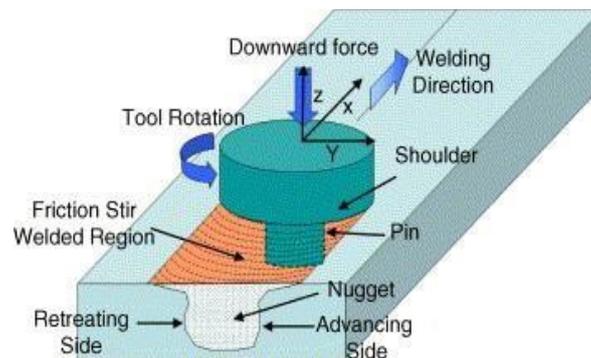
Dibujo esquemático de la soldadura por fricción y agitación. .
